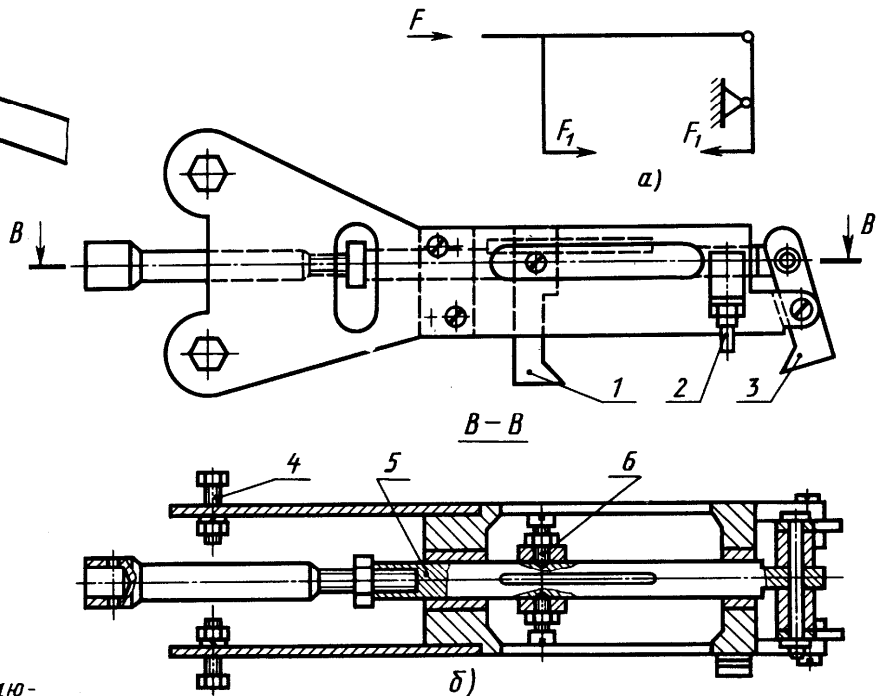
Трехпалый захват: а - схема; б - конструкция
